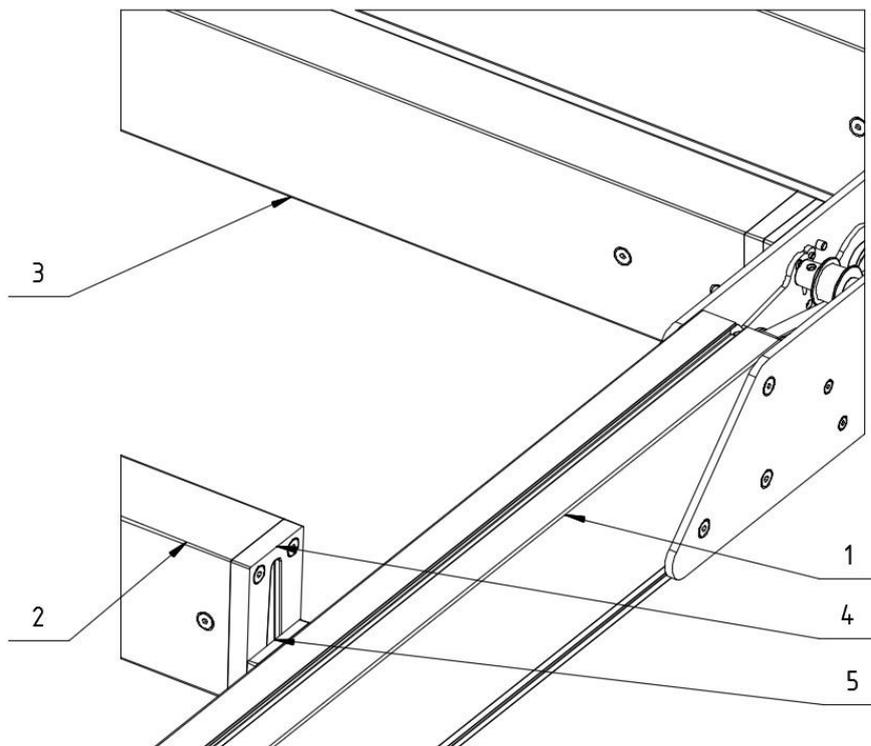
Montage des poutres des radissement : 1 – Poutre de guidage, 2 – Poutre de radissement (avant), 3 – Poutre de radissement (arrière) , 4 – Pochette Sherpa, 5 - Sherpa.
